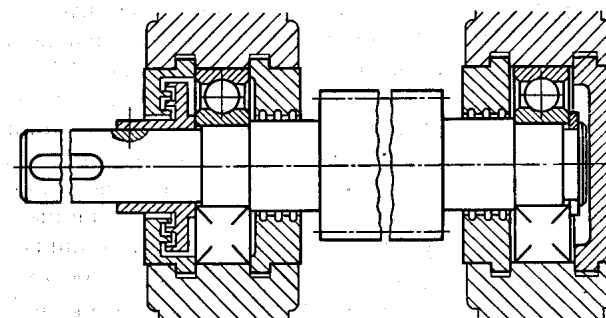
Вал установлен на радиальных подшипниках: крышки – врезные, правый подшипник – «плавающий»
